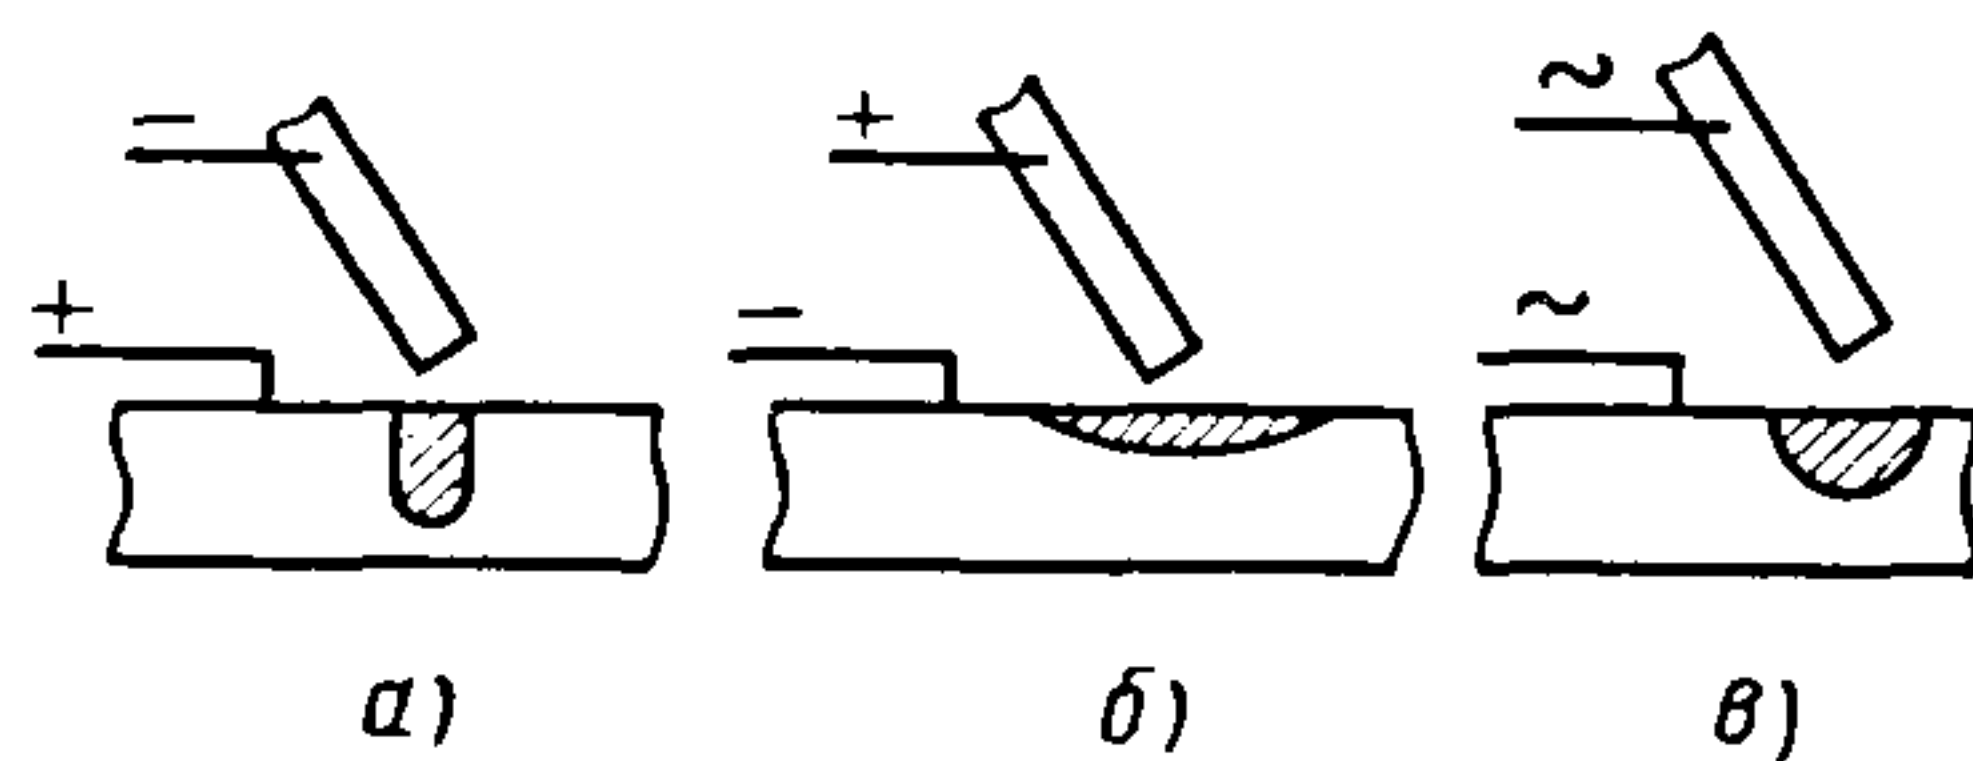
Виды проплавления при дуговой сварке:
